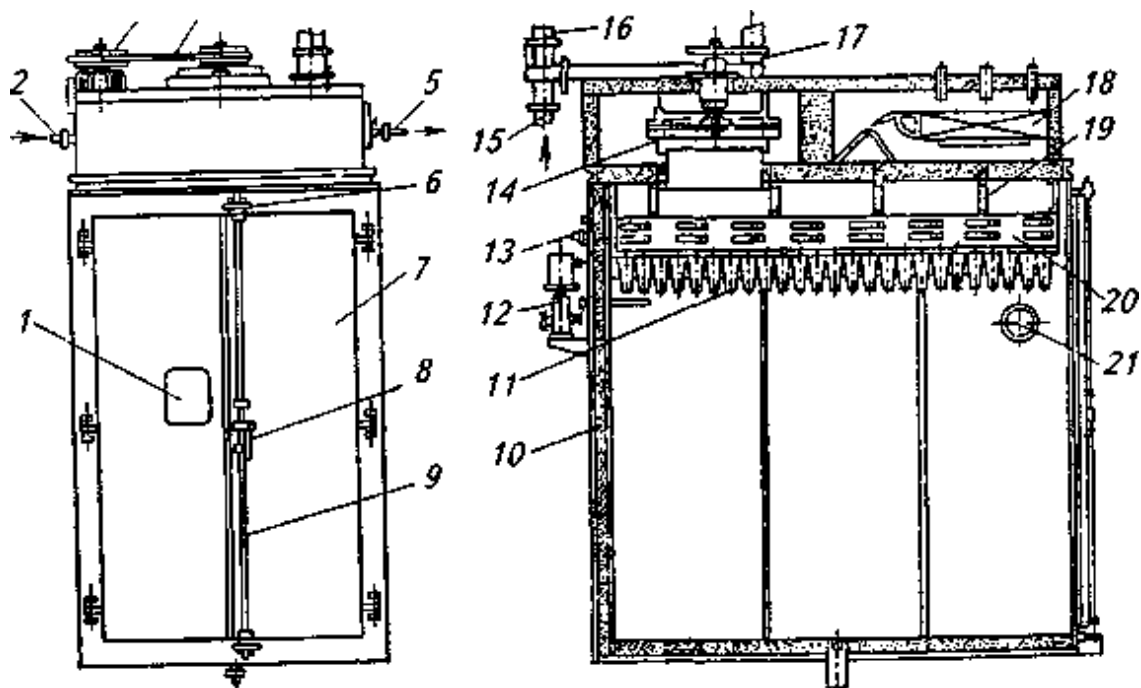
Универсальная термокамера: а – вид спереди; б – разрез: 1 – окно; 2 – паропровод; 3 – электродвигатель; 4 – клиновый ремень; 5 – трубопровод для конденсата; 6 – защелка; 7 – дверь; 8 – дверная ручка; 9 – штанга; 10 – стенка; 11 – сопла; 12 – привод; 13 – трубопровод для острого пара; 14 – вентилятор; 15 – дымоход; 16 – трубопровод для свежего воздуха; 17 – труба для отработавшего воздуха; 18 – калорифер; 19 – балки подвесного пути; 20 – всасывающая труба; 21 – лампа.
